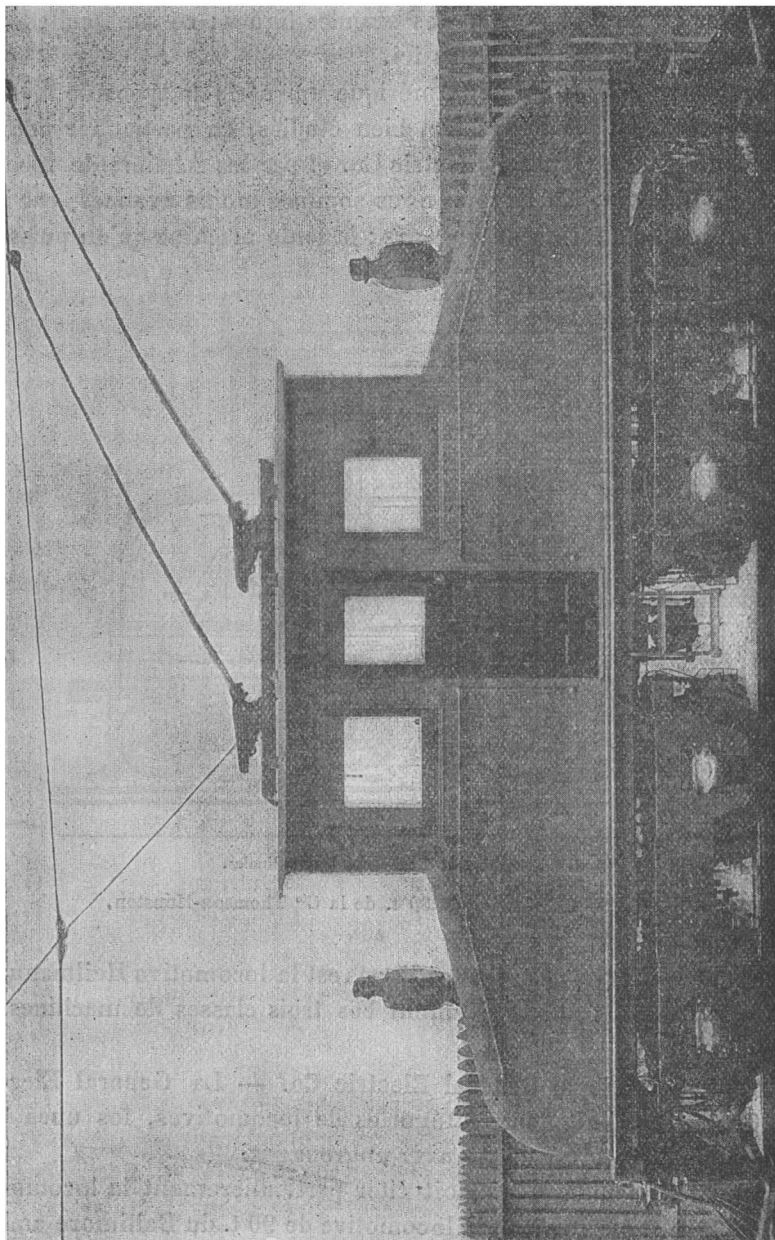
Locomotive de 40 t. à engrenages de la General Electric Co.
